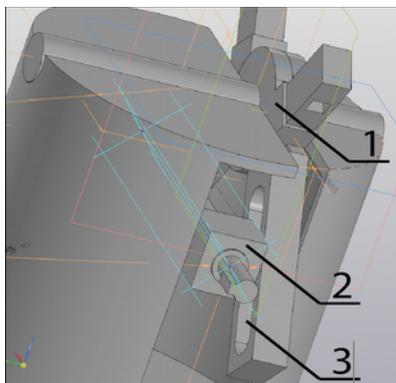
Универсальный инструмент сжатия с тремя насадками (ножницы, инструмент захвата шестигранных гаек и болтов, клещи) использует конструкцию (1), похожую на ножницы, плоскогубцы и т. д., но с прорезями в ручках (3), в которые вставлены штыри (2) с резьбовыми отверстиями.
